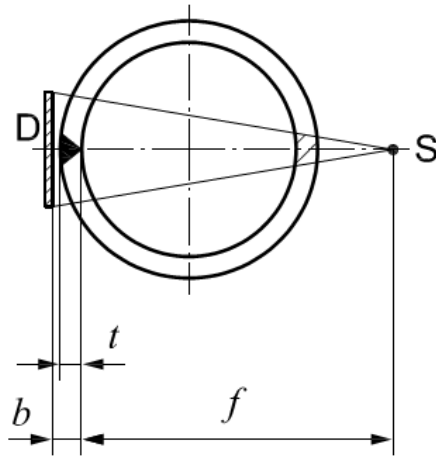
Схема контроля прямолинейного сварного шва при просвечивании через две стенки (одно изображение)
